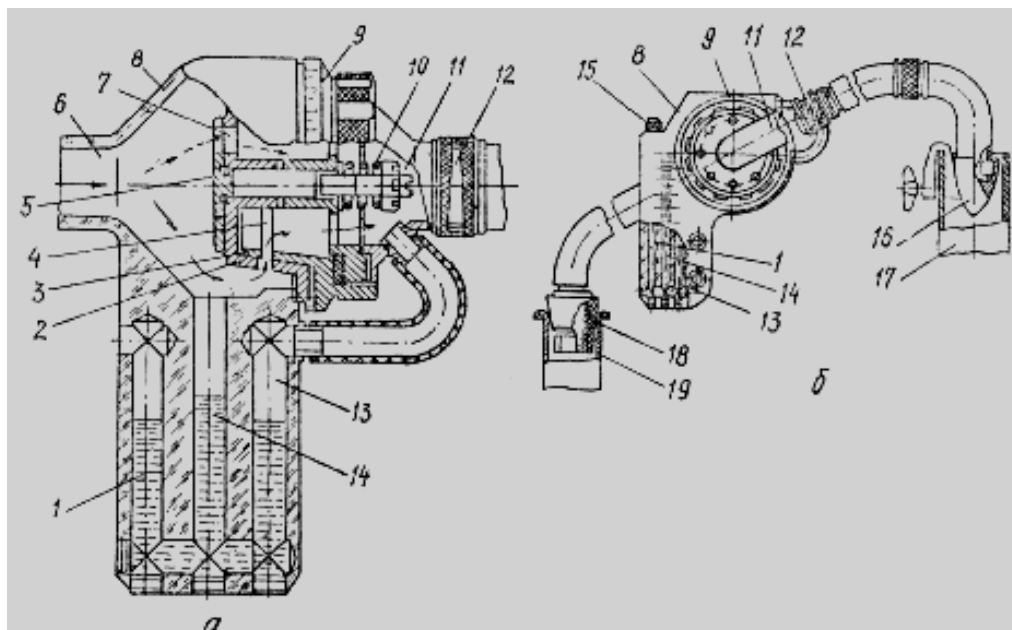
Пристрій для вимірювання витрати газів КИ-4887:
